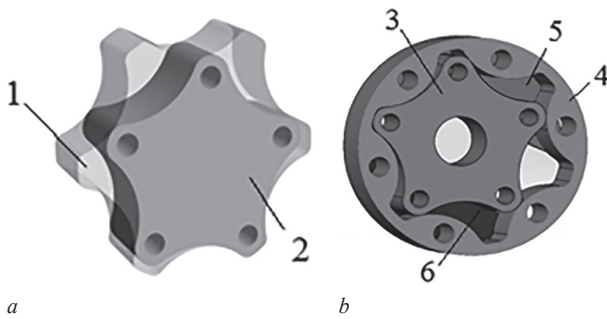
Расчетные области масляного героторного насоса (а) и модели элементов насоса (б): 1 — область жидкости; 2 — область твердого тела; 3 — внутренний ведущий ротор; 4 — внешний ведомый ротор; 5 — патрубок высокого давления; 6 — патрубок низкого давления
